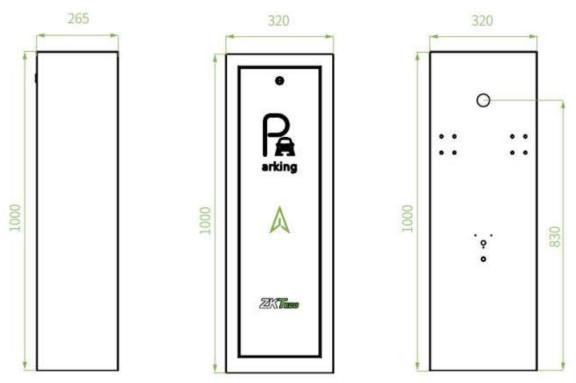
Габаритные размеры корпуса шлагбаума (в мм)
